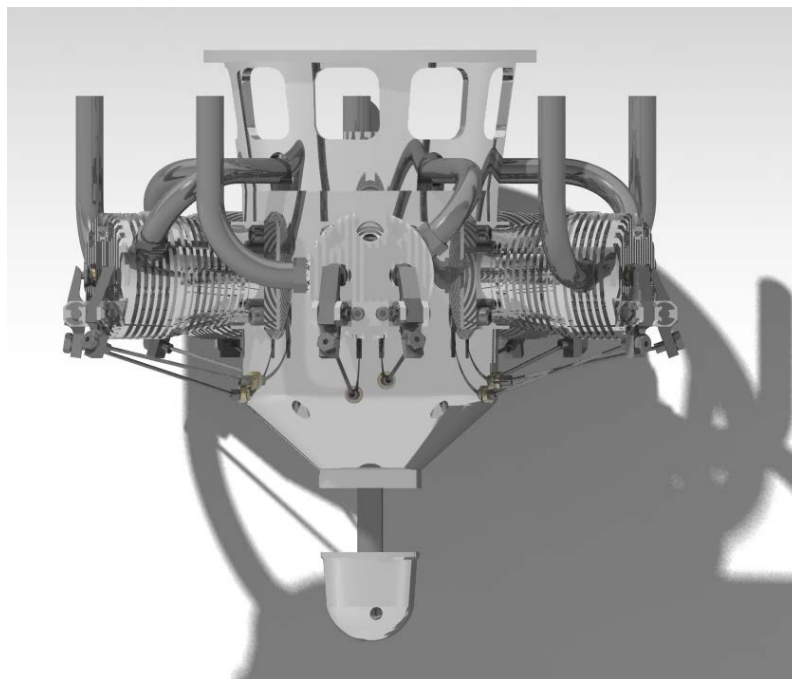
Vista en planta del ensamblaje final renderizado en Catia V5.
